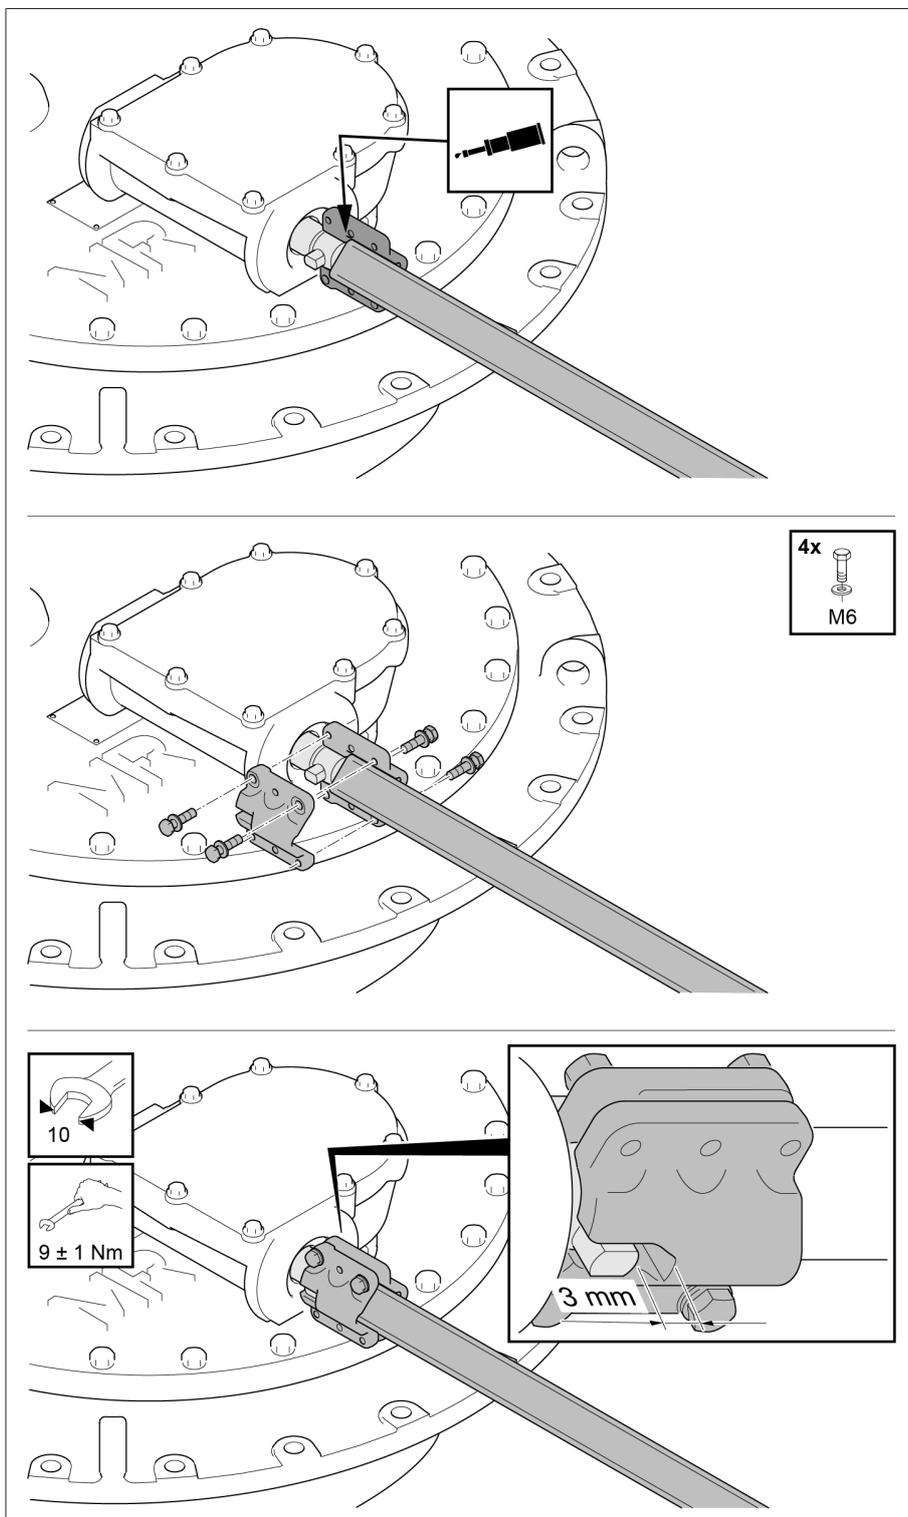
Prender o tubo quadrado à caixa de engrenagem superior
